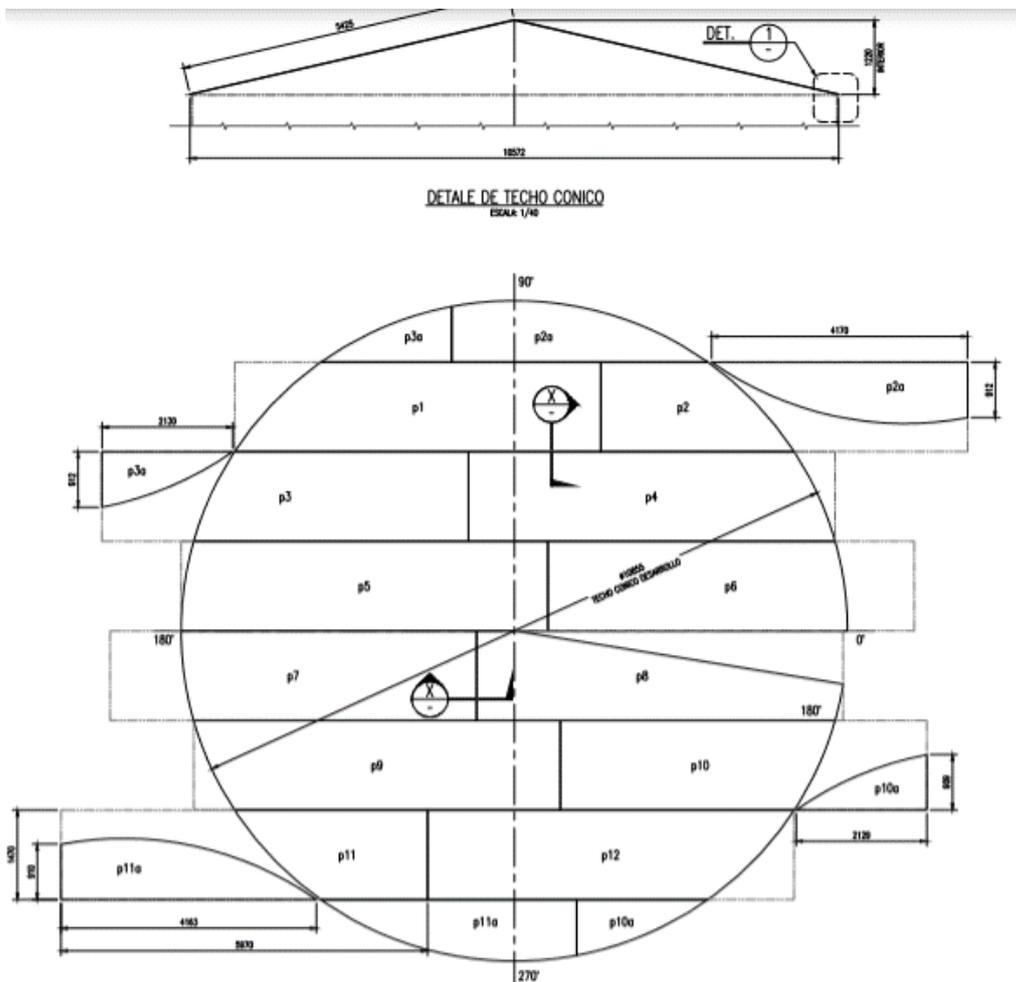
Mapa de soldadura de un techo cónico de un tanque.
